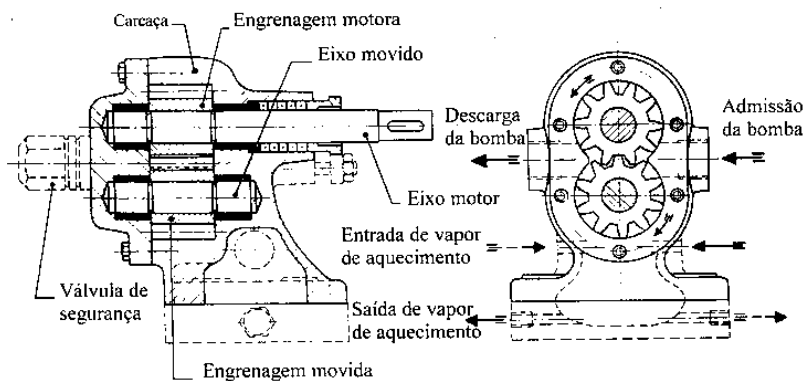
Bomba de engrenagens com camisa de aquecimento a vapor (Fonte: Intersigma).
